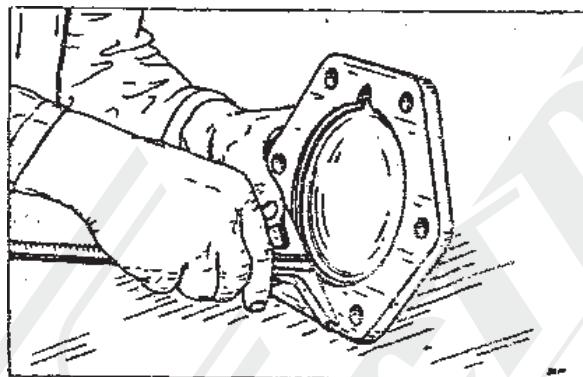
Измерение расстояния от установочной поверхности крышки до установочной поверхности подшипника.
